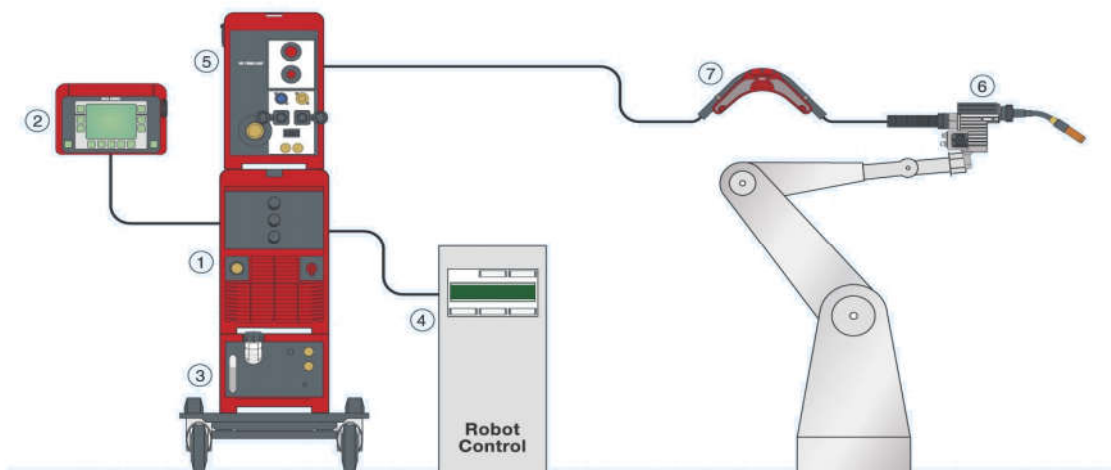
Schweißanlage (Quelle: [www.fronius.com](http://www.fronius.com))
